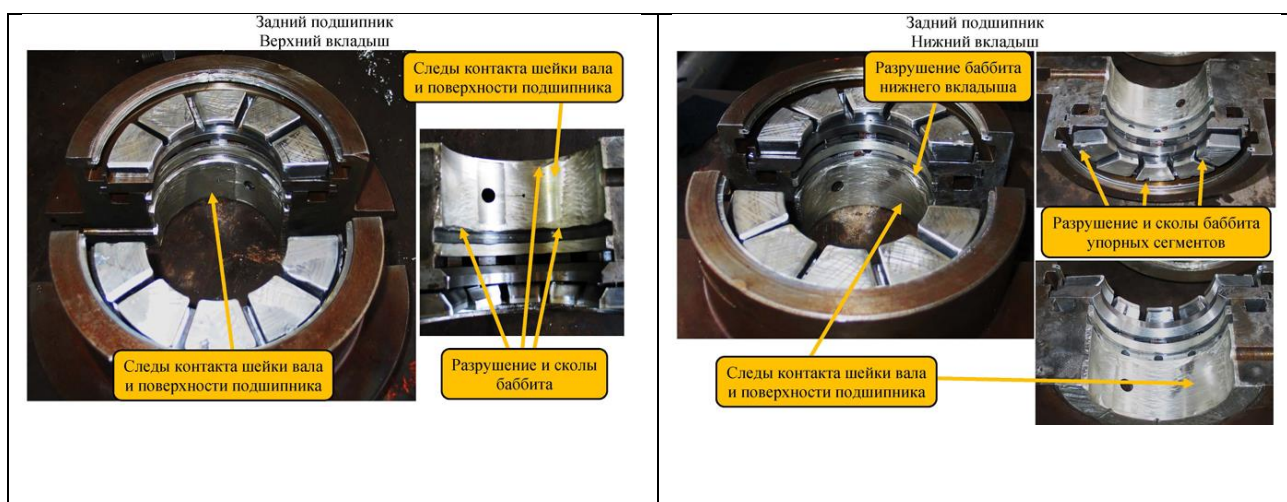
Детали заднего подшипника компрессора: следы контакта шейки вала и поверхности верхнего и нижнего вкладышей со сколами и разрушением баббита вкладышей, разрушение баббита упорных сегментов
